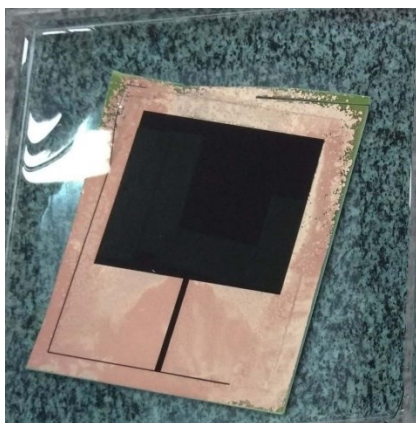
Placa impressa durante o processo de corrosão. Fonte: [Autoria própria].
